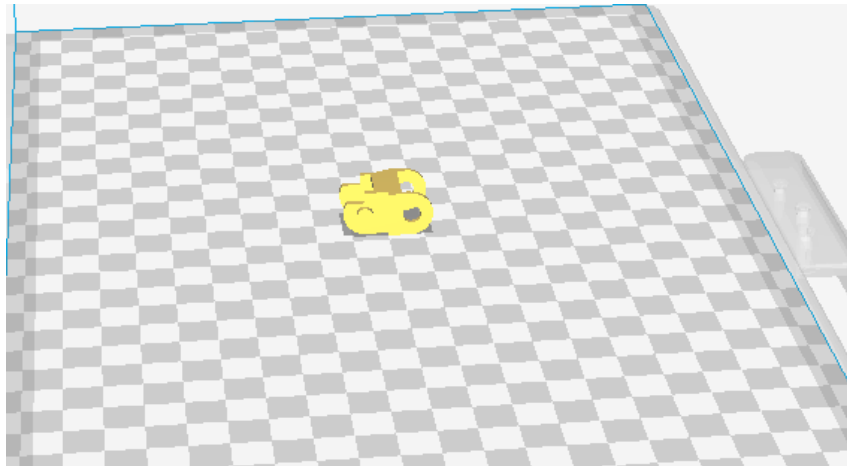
Posición de impresión de una de las piezas que forma el conjunto de la cadena portacable 1.
